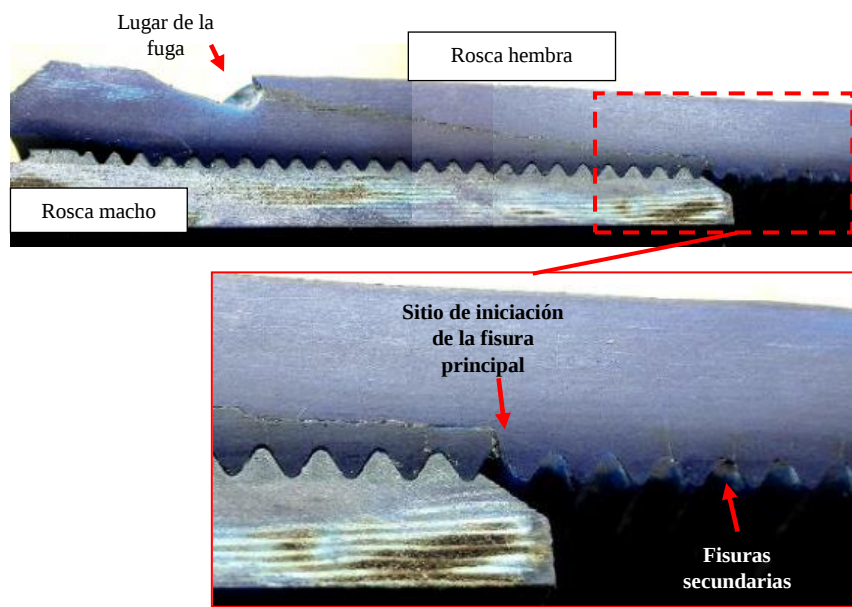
Corte longitudinal del defecto "C". Se observa el lugar de iniciación de la fisura principal, la propagación en el espesor y el lugar de la fuga. Se aprecian fisuras secundarias.
